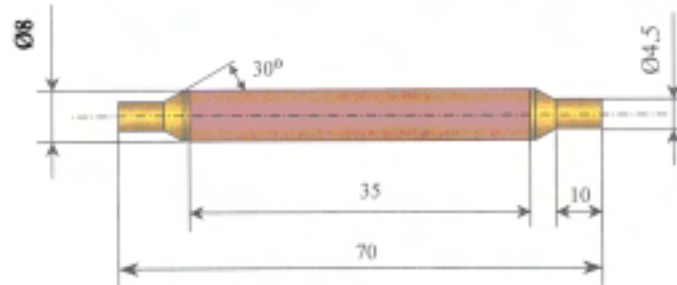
Probengeometrie für die Kreisläufe bei IPPE, Angaben in mm
